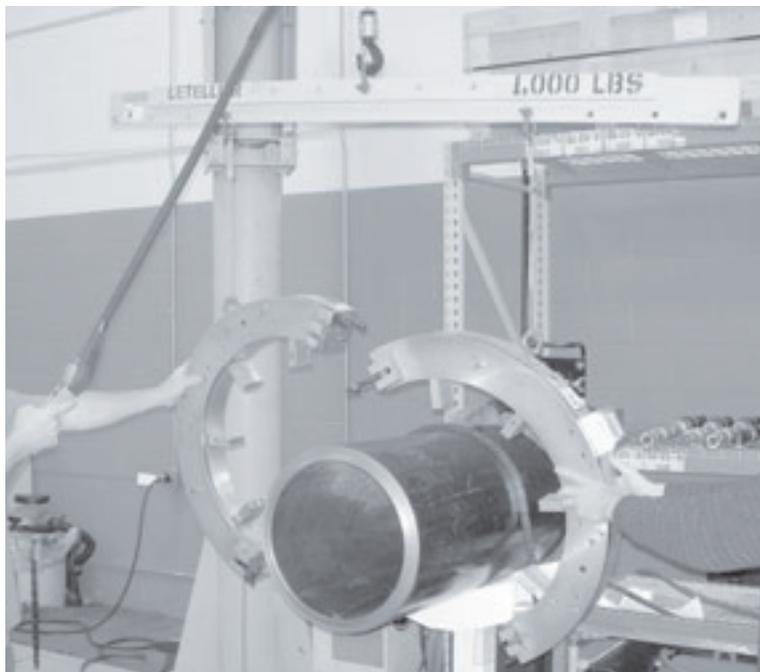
Montare le due metà dell'anello attorno al tubo come mostrato.
